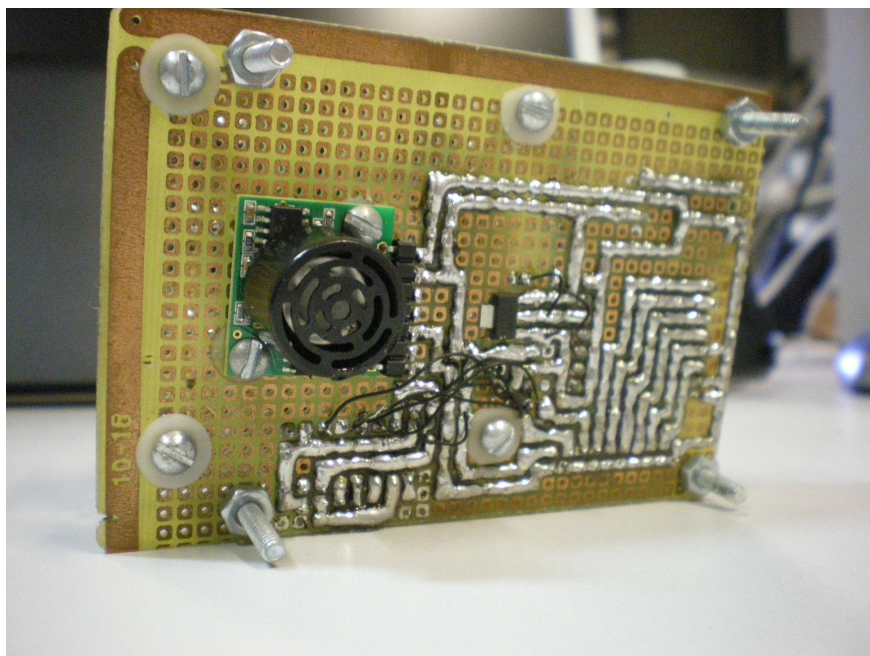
Destaque do sonar montado sob a placa dos sensores.
